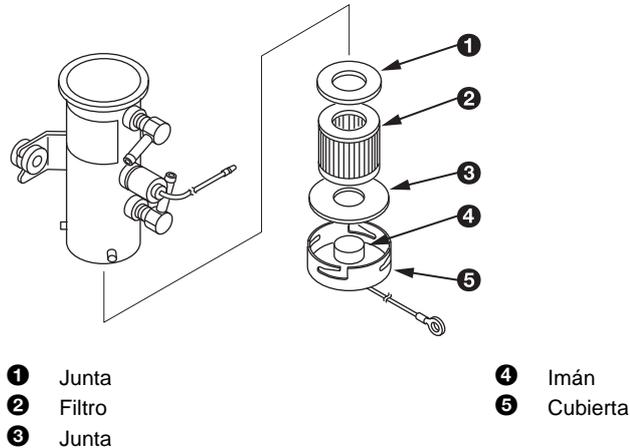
Filtro de la bomba de combustible de solenoide - Sustitución
